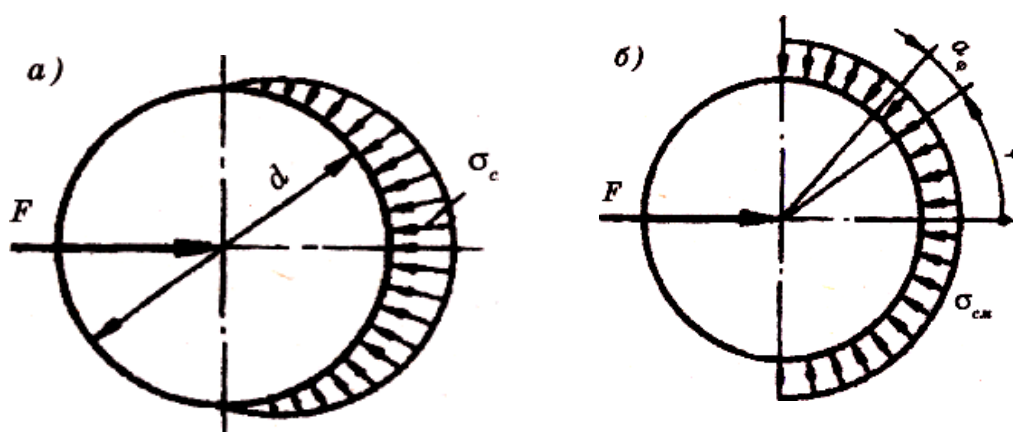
Распределение напряжений смятия по цилиндрической поверхности контакта болта и детали
